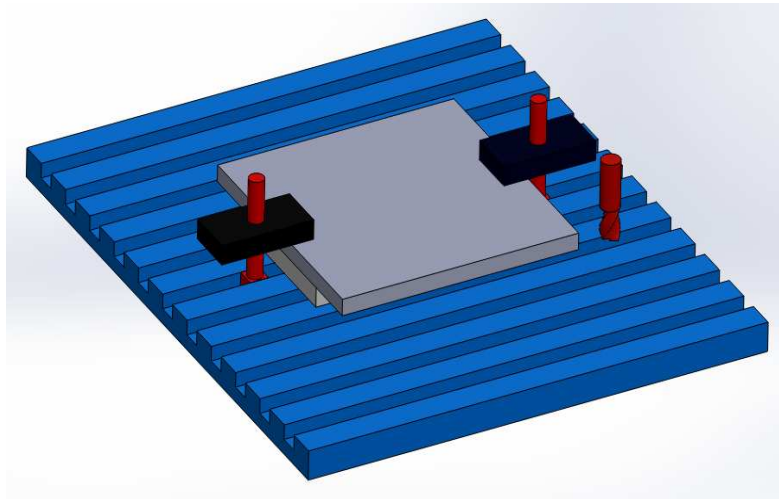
Primeira fixação antes de proceder à maquinagem da placa superior.
